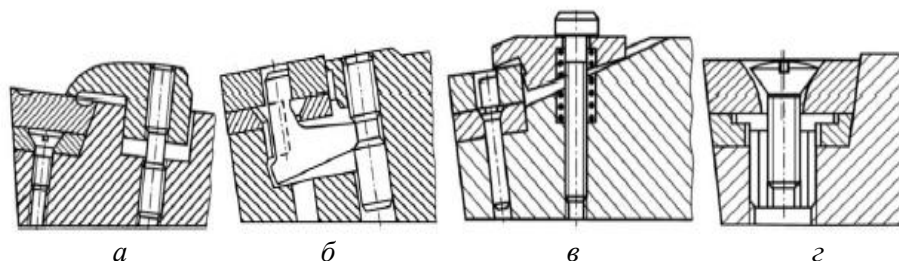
Различные схемы крепления твердосплавных пластин на токарных державках:
